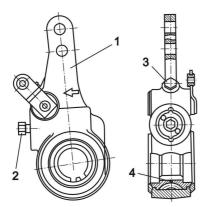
Регулятор тормоза РТ-40 1- корпус регулятора; 2- фиксатор; 3- пробка; 4-отверстие для выхода смазки
